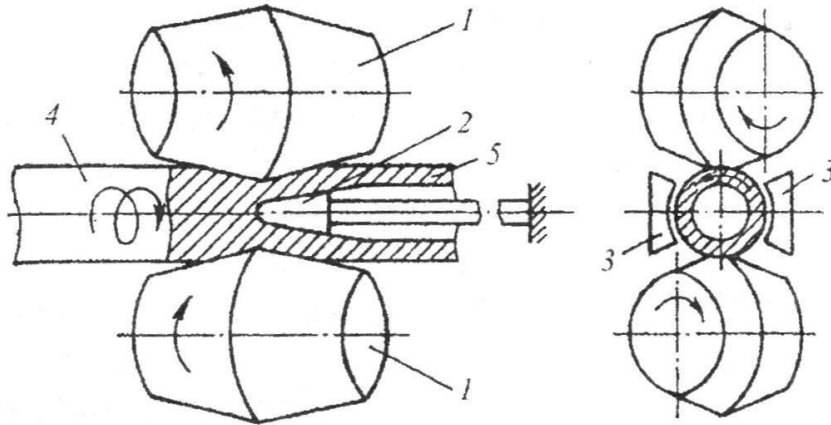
Схема косоного прокатування при прошиванні заготовки:
